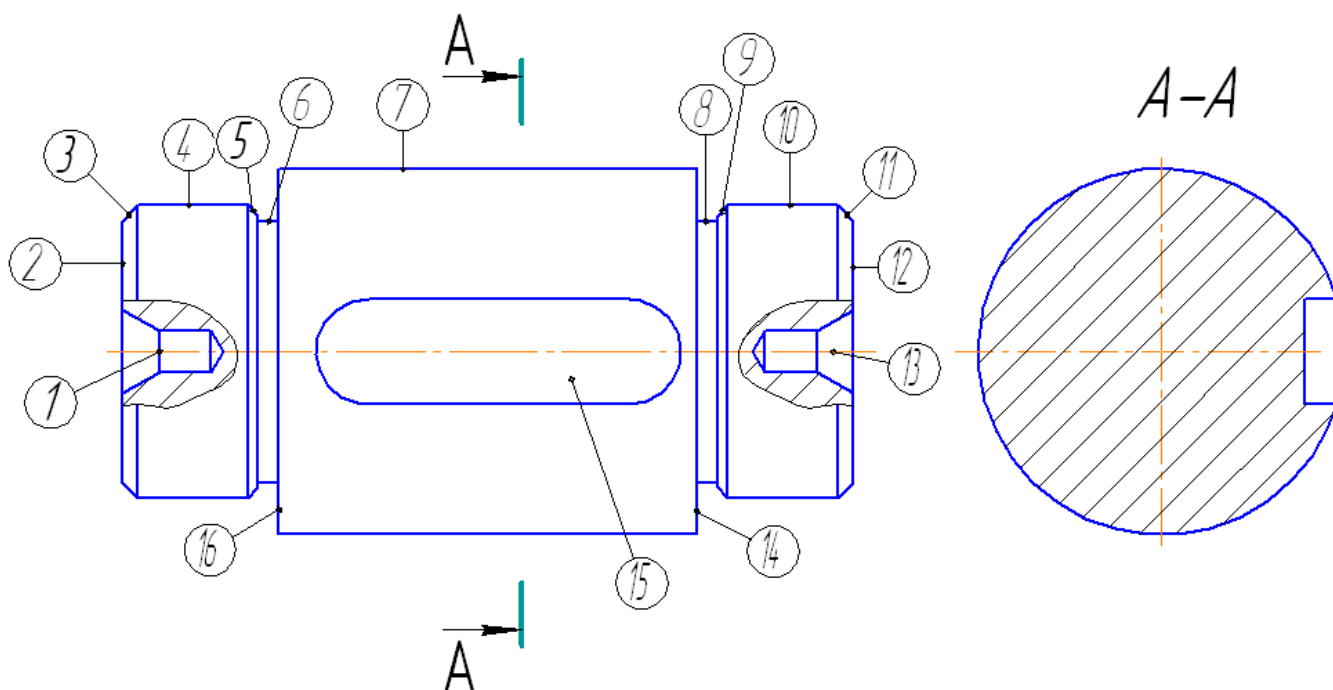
Ескіз деталі із номерами поверхонь.
